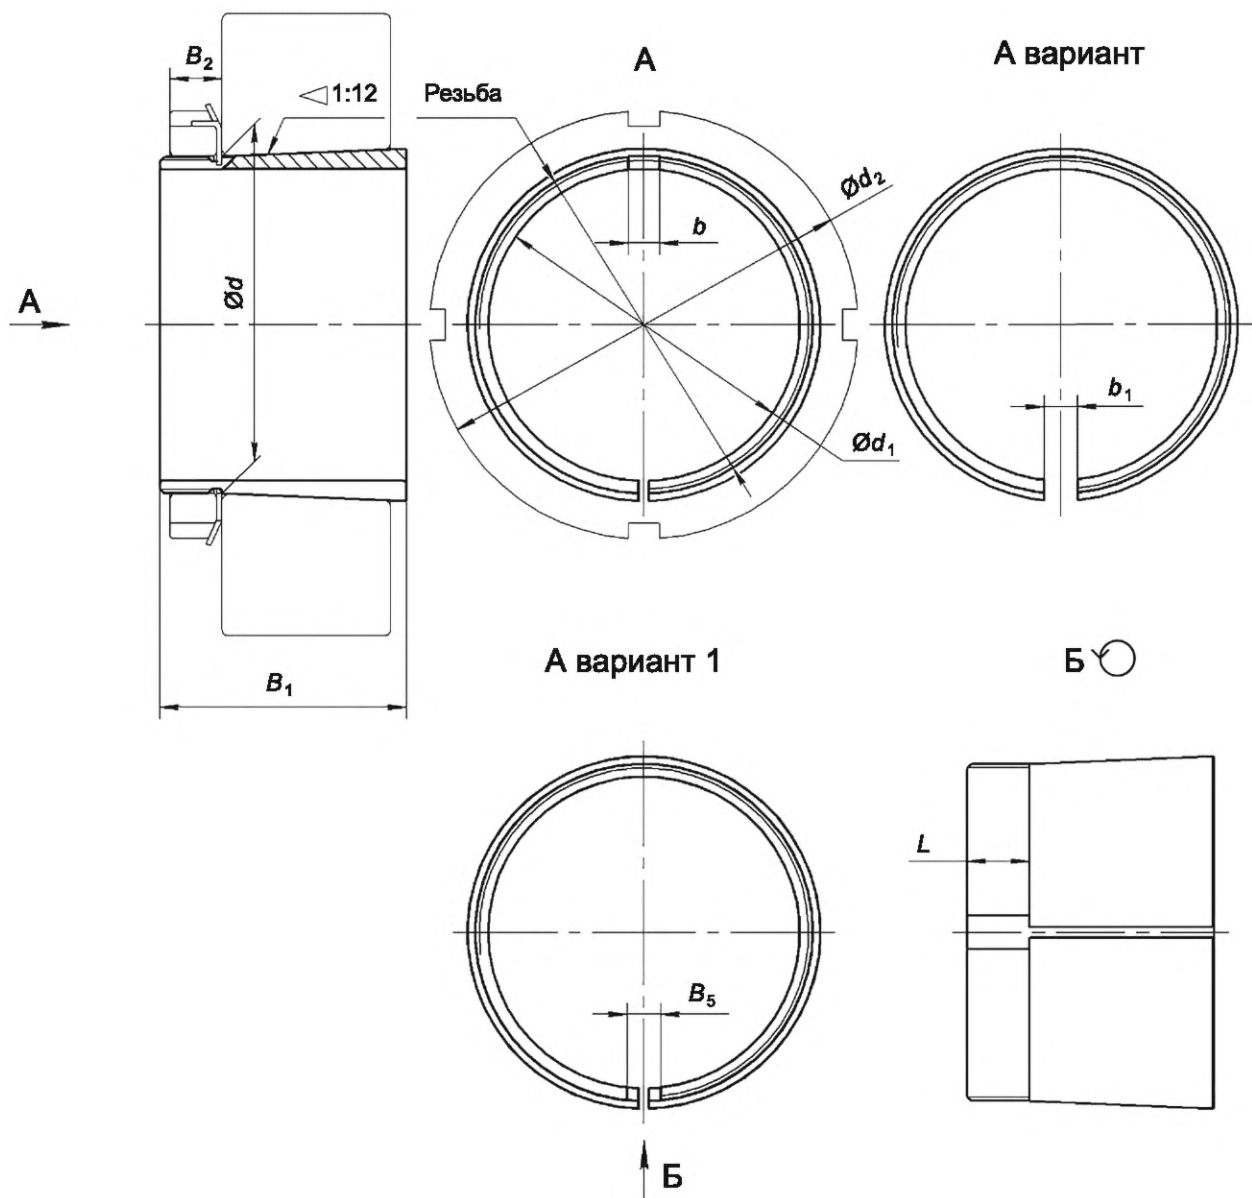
Закрепительная втулка, предназначенная для монтажа подшипника с помощью стопорной гайки и стопорной шайбы
